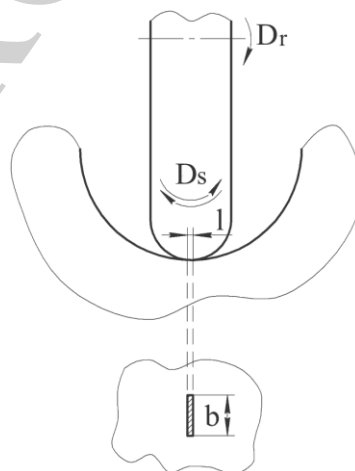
Схема контакту інструмента й заготовки при фрезеруванні зі зворотньо-гойдаючим рухом подачі
